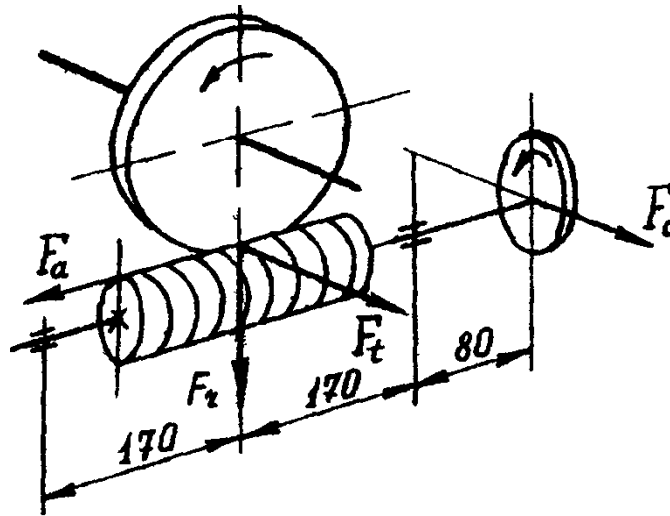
Расчетная схема входного вала червячного редуктора
